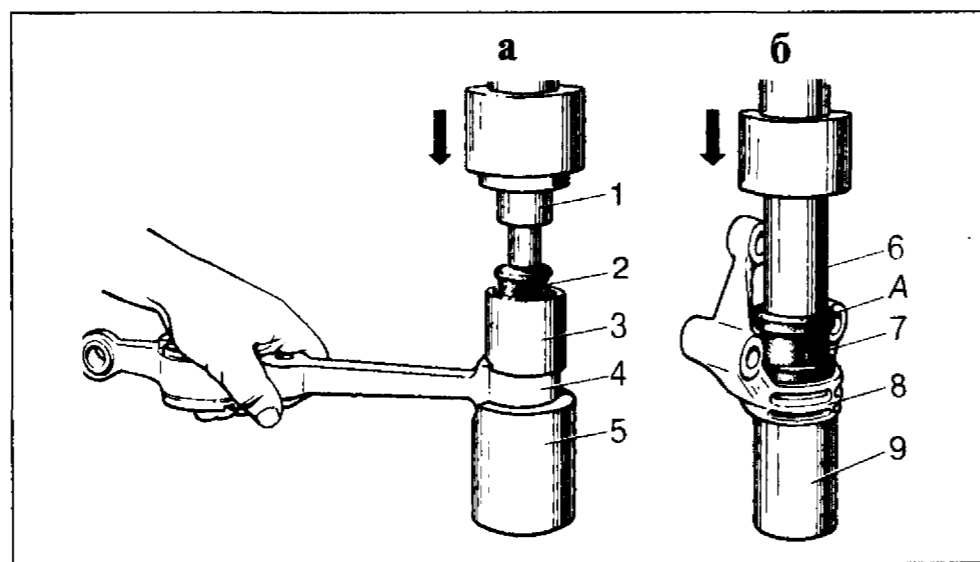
Запрессовка резинометаллических шарниров: рычага подвески (а) и кронштейна крепления растяжки (б): 1 — оправка; 2 — резинометаллический шарнир; 3 — направляющая втулка; 4 — рычаг подвески; 5 — опорная втулка; 6 — оправка; 7 — резинометаллический шарнир; 8 — кронштейн крепления растяжки; 9 — опорная втулка
